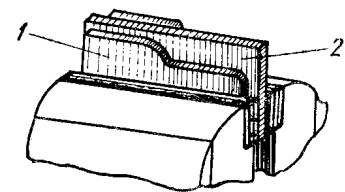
Обробка деталі в обпилювальному кондукторі (копірі): 1 – копірна планка, 2 – заготовка
